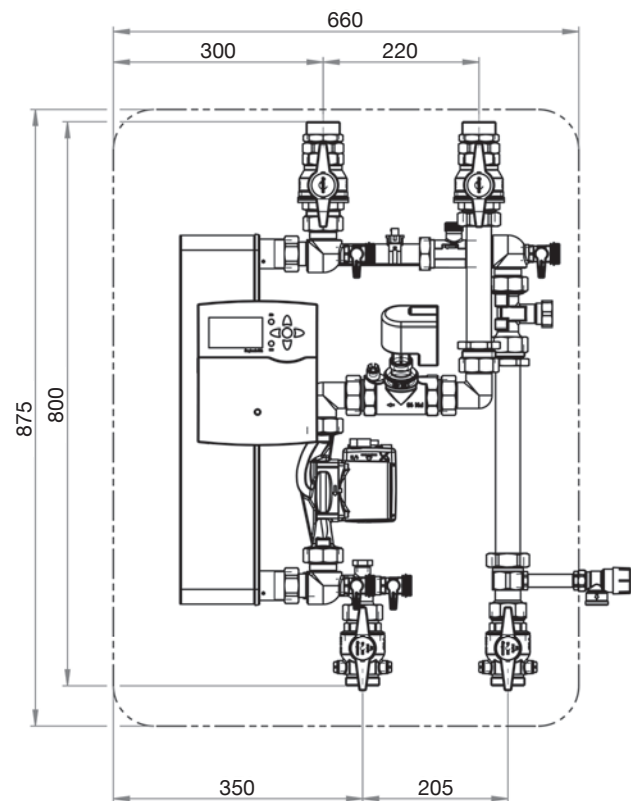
Dimensiones “Regumaq X-80” (frontal)
